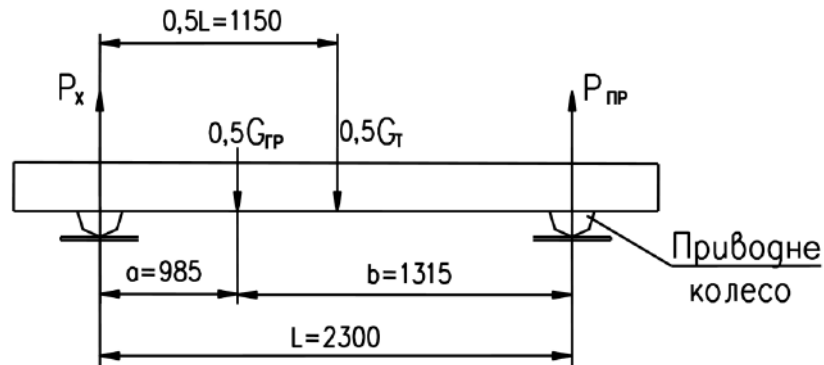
Схема навантажень на кінцеву балку візка при пересуванні з вантажем
